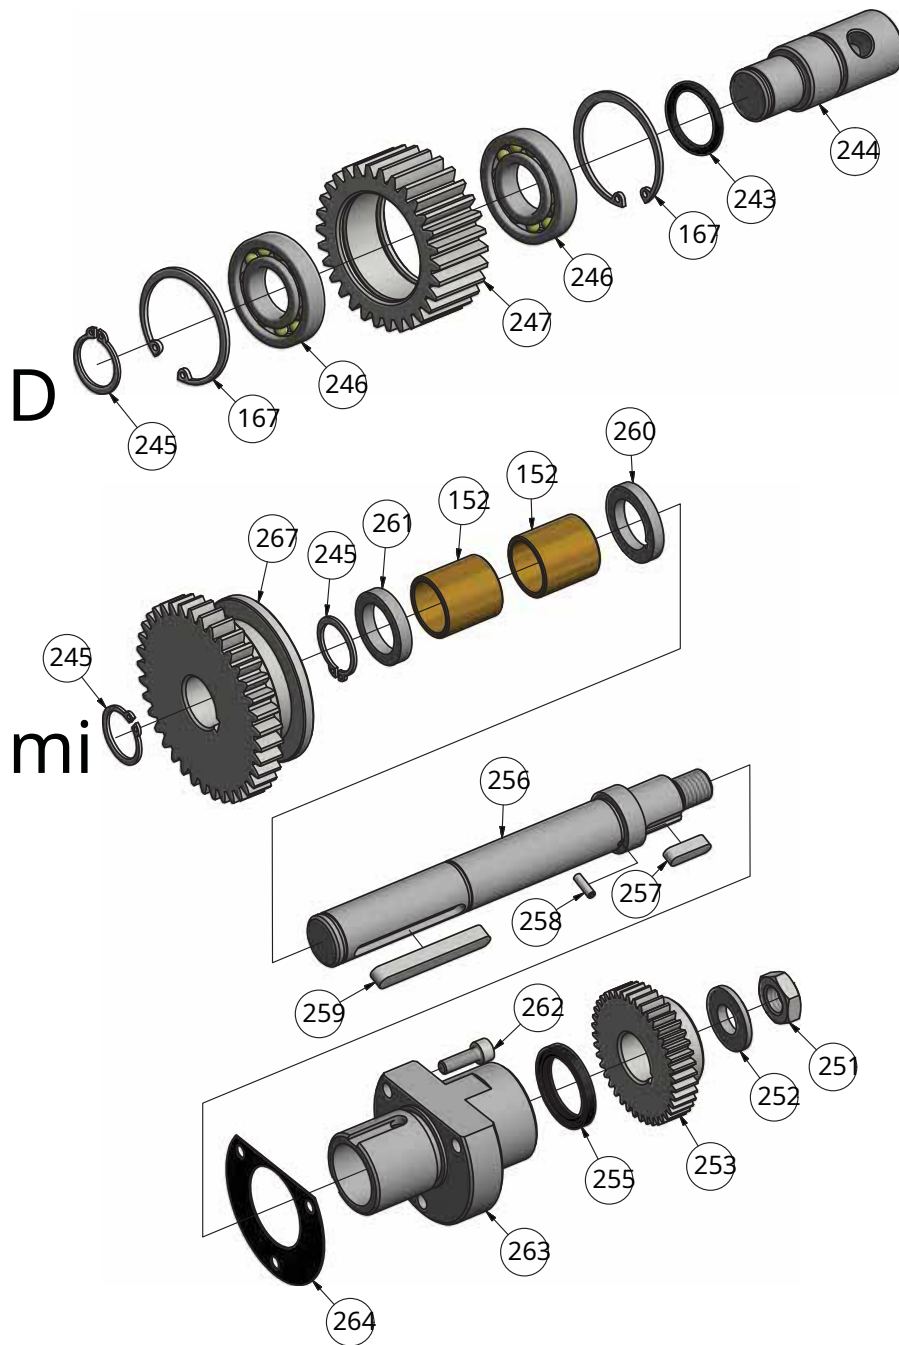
Getriebe Spindelstock 5-6 - Engranaje del cabezal 5-6
